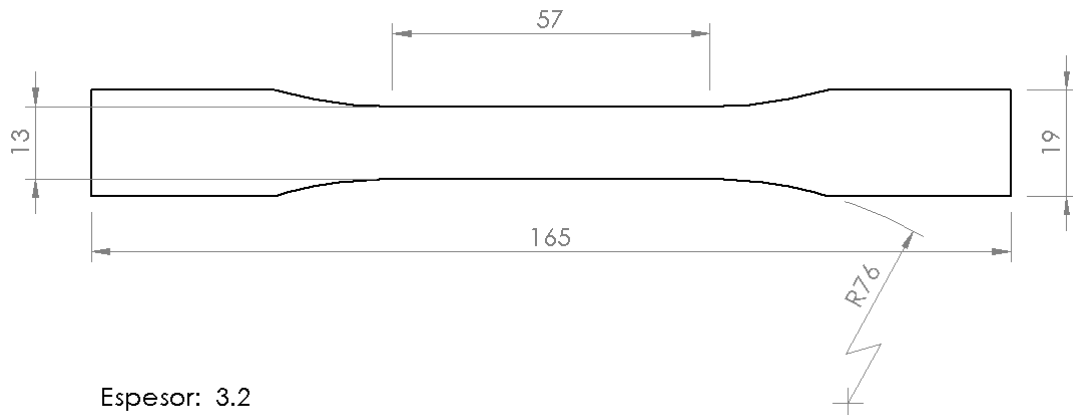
Dimensiones finales de la probeta de ensayo a tracción en unidades de mm [70].
